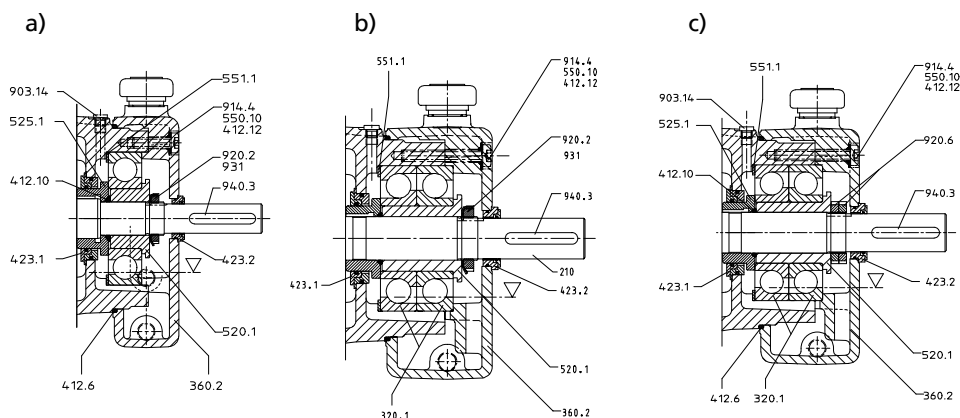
Масляная смазка и лабиринтное уплотнение: а) типоразмер 32 и б) типоразмер 50-65 и с) типоразмер 100-150
